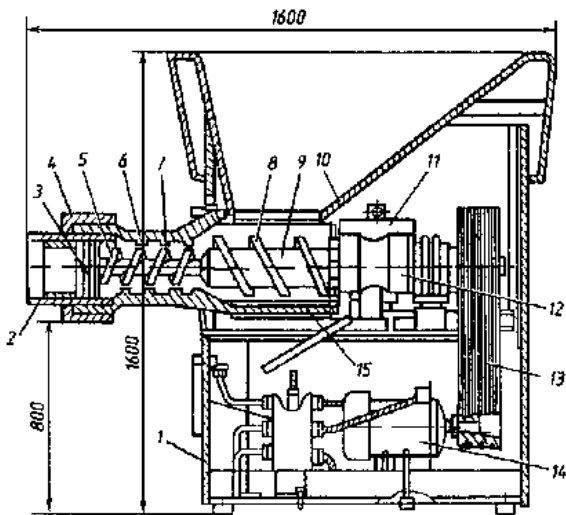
Вовчківка К6 ФВП 120: 1 - станина; 2 - гільза; 3 - ріжучий механізм; 4 - накидна гайка; 5 - подавальний шнек; 6 - корпус циліндра; 7 - ребро; 8 - живильний шнек; 9 - суцільний вал; 10 - завантажувальна горловина; 11 - мотор-редуктор; 12 - корпус підшипників; 13 - клинопасова передача; 14 - електродвигун; 15 - корпус шнеків
